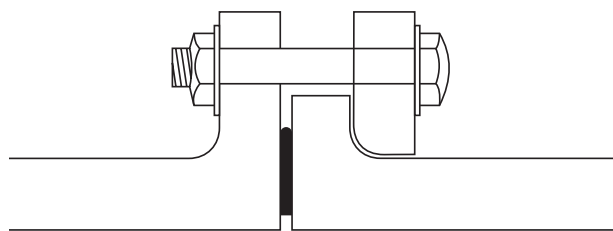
Losflansch mit flacher Dichtung inkl. Stahleinlage
